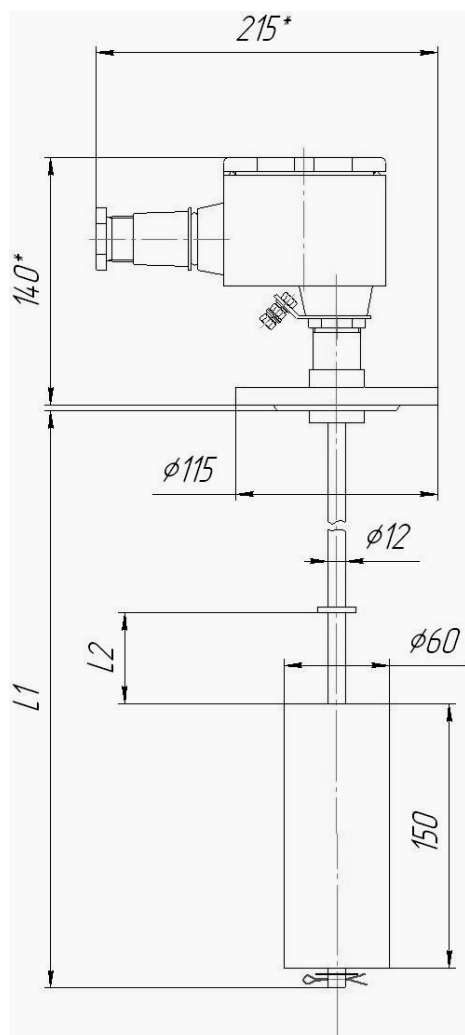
Габаритные и установочные размеры сигнализатора СЖУ-1-ПВ
